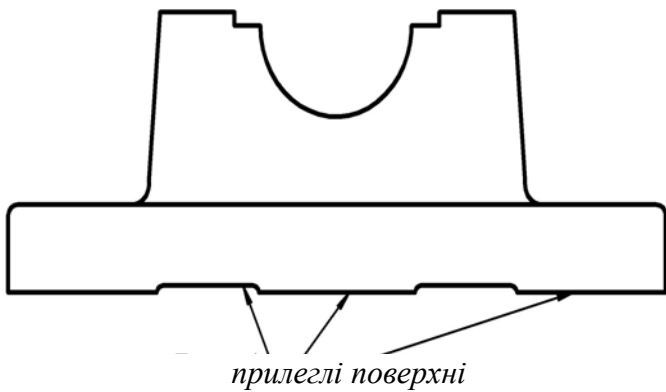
Робоче положення деталі, прийняте для зображення головного виду кресленника
